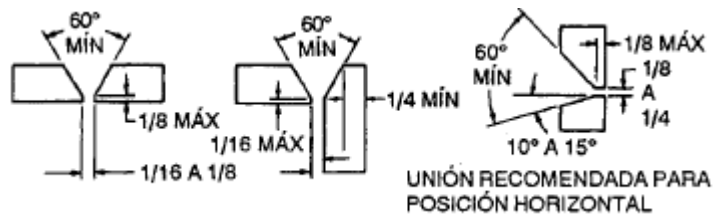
Juntas soldadas a tope con bisel.
